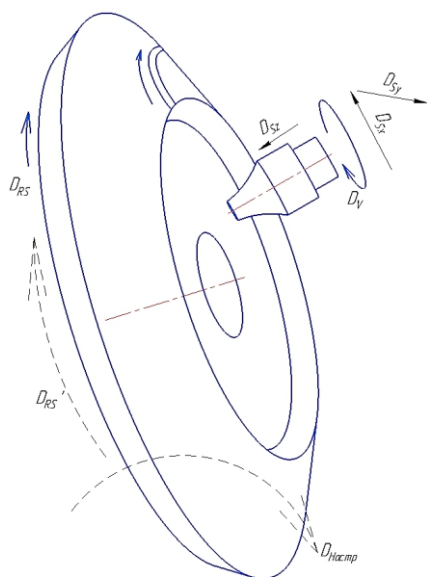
Совокупность движений при нарезании зубьев конического зубчатого колеса с криволинейным зубом
